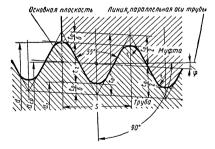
Профиль трубной конической резьбы по ГОСТу 6211—52
